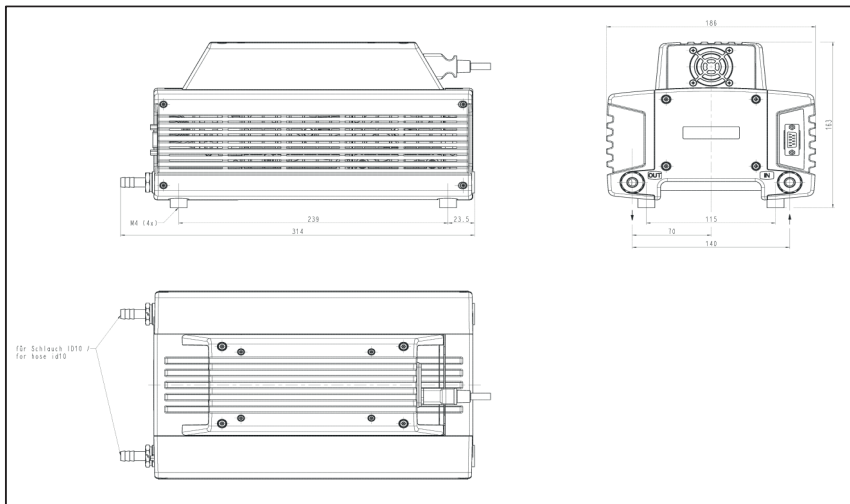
Befestigungsmaße Pumpe PJ25481-950.50.18
